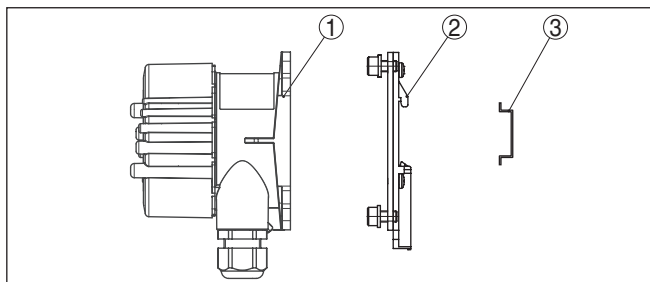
VEGADIS 82 con carcasa de aluminio y acero inoxidable para el montaje en regleta de montaje
